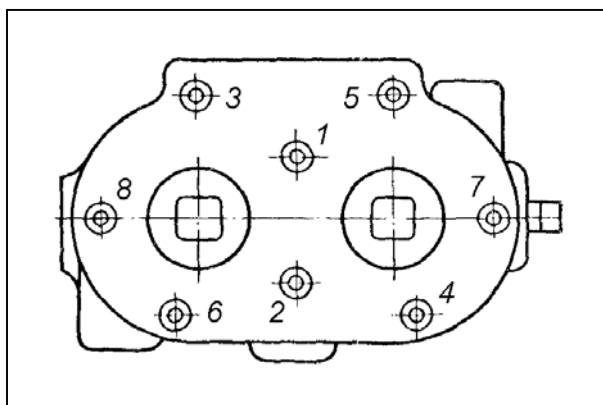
Последовательность затяжки гаек крепления головки цилиндров компрессора.
